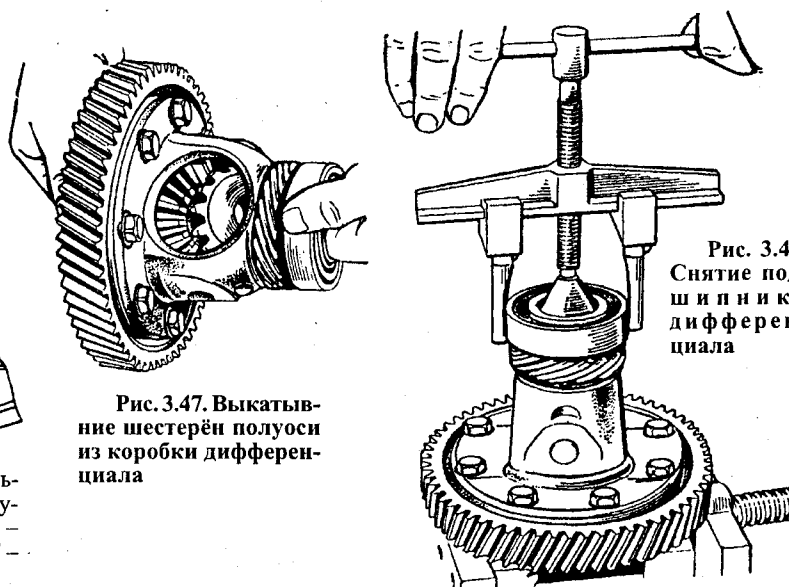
Выкатыние шестерён полуоси из коробки дифференциала
